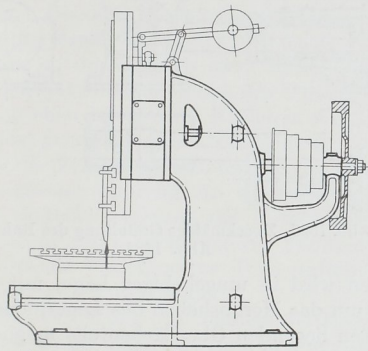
Ständer einer Stoßmaschine neuerer Form.
